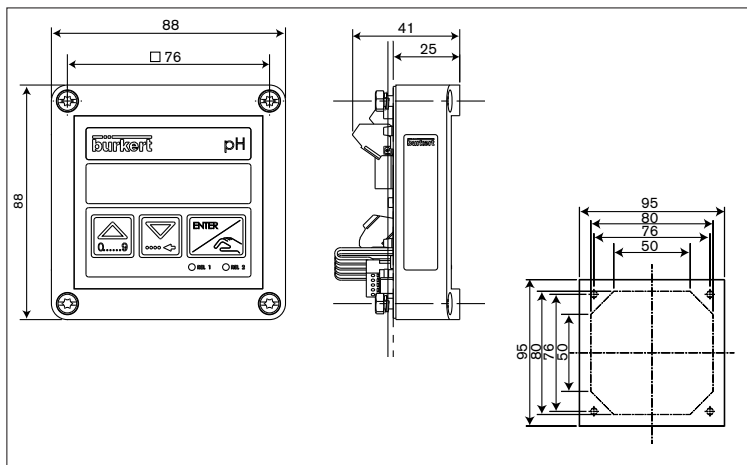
Dimensions transmetteur de pH 8205 encastrable et du masque de découpe
